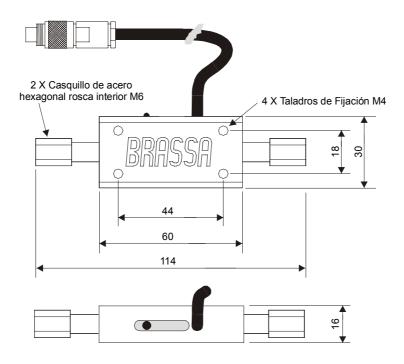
Dimensiones Captador de Posición CSEM-C-01
